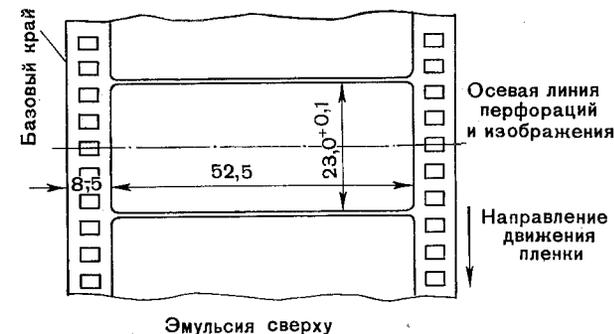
Размеры и расположение негативного изображения широкоформатного фильма на 70-мм киноплёнке
